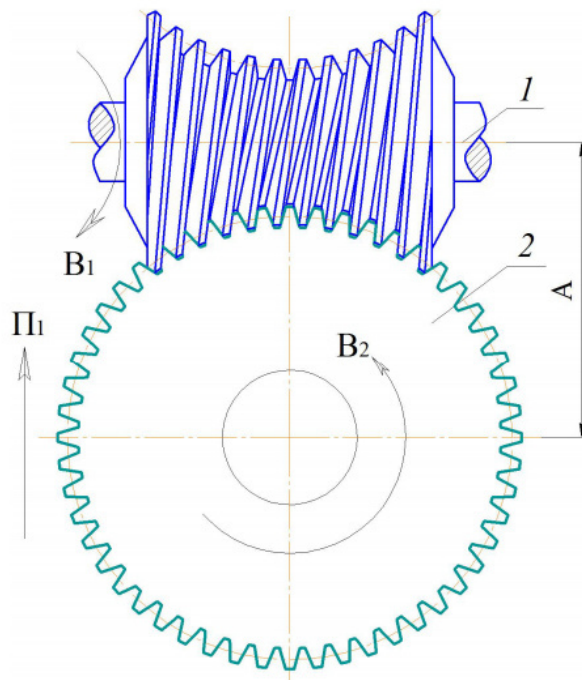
Схема багаторізцевої головки для нарізування ВП глобоїдного черв'яка при радіальній подачі інструменту: 1 - заготовка глобоїдної черв'яка; 2 - інструмент; А - міжосьова відстань; B_1 - обертання заготовки глобоїдного черв'яка; B_2 - обертання інструменту; Π_1 - радіальна подача інструменту
